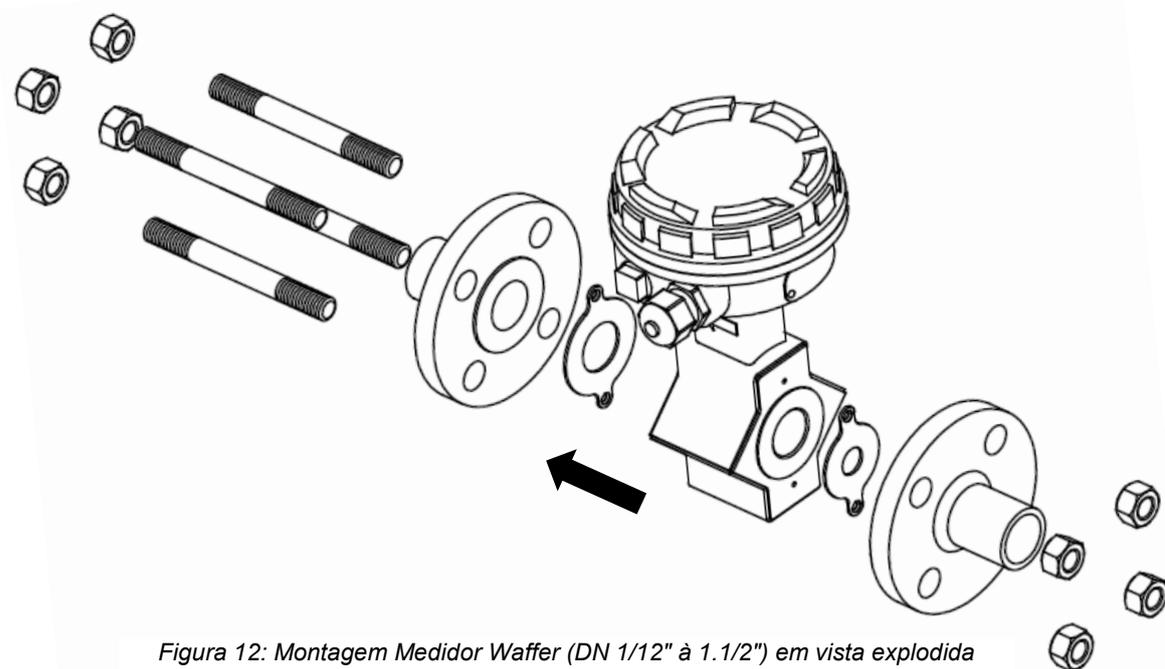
Montagem Medidor Waffer (DN 1/12" à 1.1/2") em vista explodida
